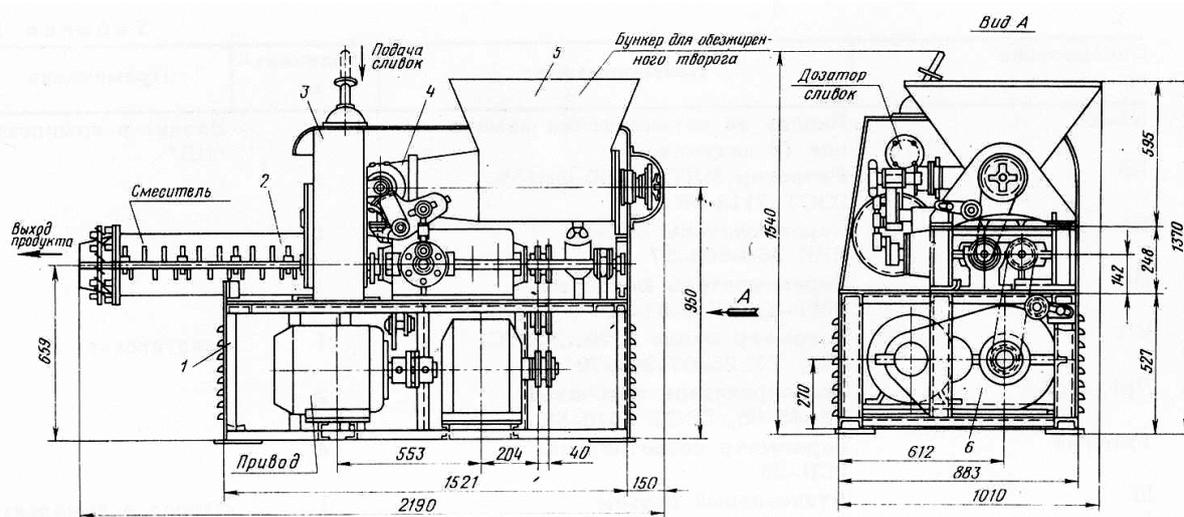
9. Общий вид смесителя с дозаторами обезжиренного творога и сливок марки ОСТ: 1 – станина; 2 – смеситель; 3 – дозатор сливок; 4 – дозатор творога; 5 – приемный бункер; 6 – привод
